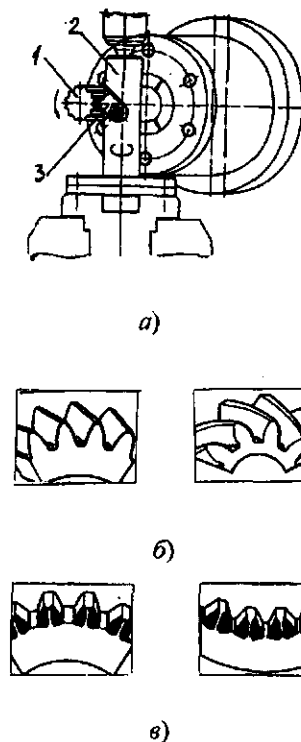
Обкатное фрезерование твердосплавными режущими пластинами: а – обкатка шлицевого вала; б – снятие фасок; в – зубозакругление
